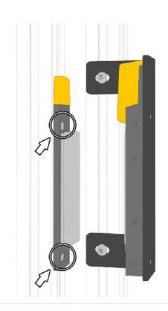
Ankerplatte am Profil der Schiebetüre anbringen, zur Prozesszuhaltung ausrichten und zur Prozesszuhaltung ausrichten. Schrauben M6 x 12 mm Torx festziehen.
